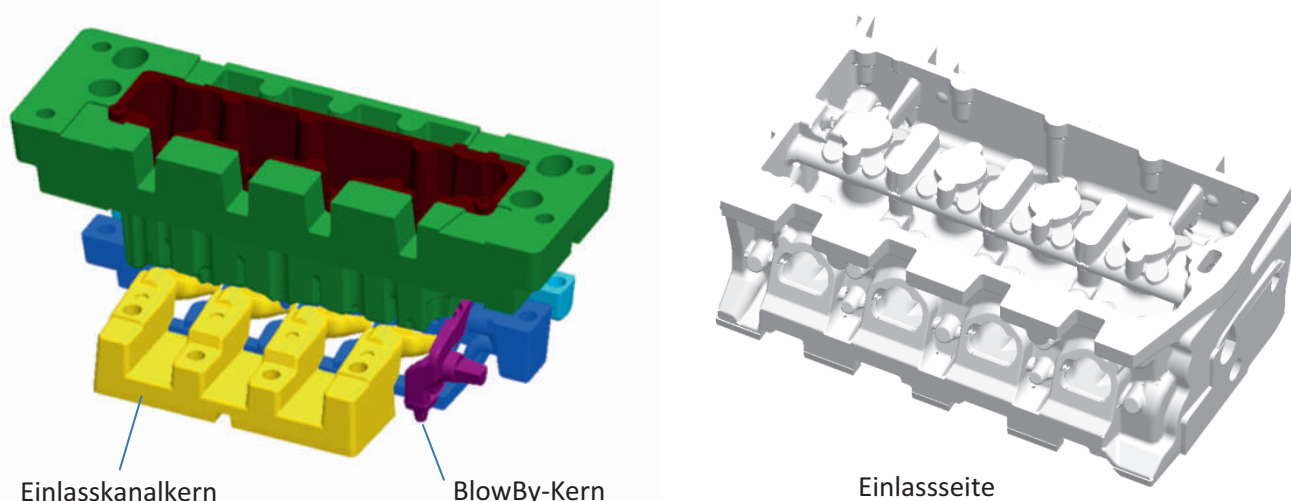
Zylinderkopf 1,4l TSI – Einlassseite mit Kernen
